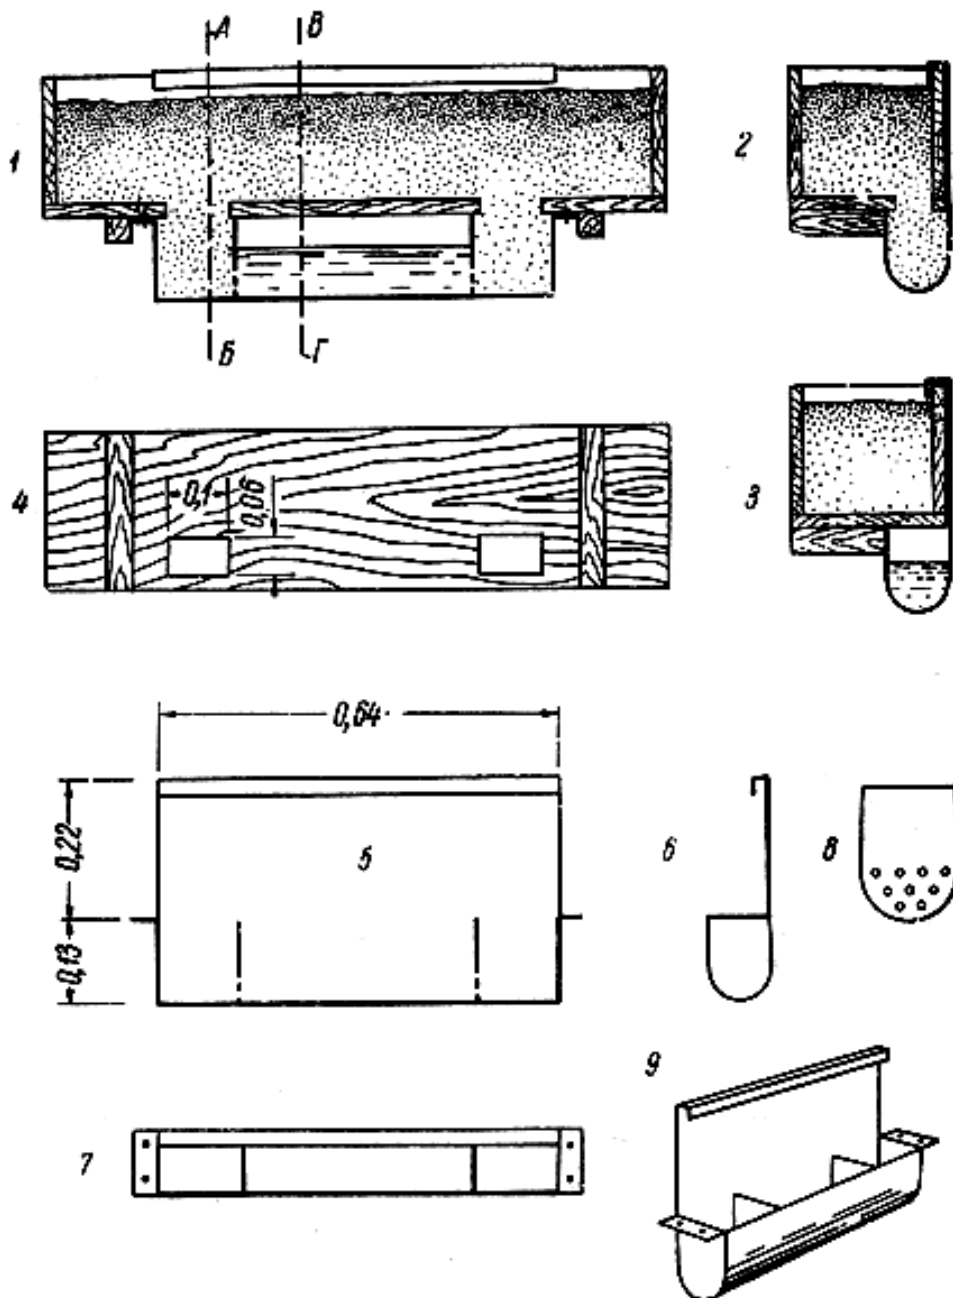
Усовершенствованный цветочный ящик (размеры в метрах): 1 — продольный разрез; 2 — поперечный разрез по АБ; 3 — поперечный разрез по ВГ, 4 — вид снизу. Резервуар для избыточной влаги; 5 — продольный разрез; 6 — поперечный разрез; 7 — вид сверху; 8 — устройство внутренних перегородок резервуара; 9 — общий вид резервуара
